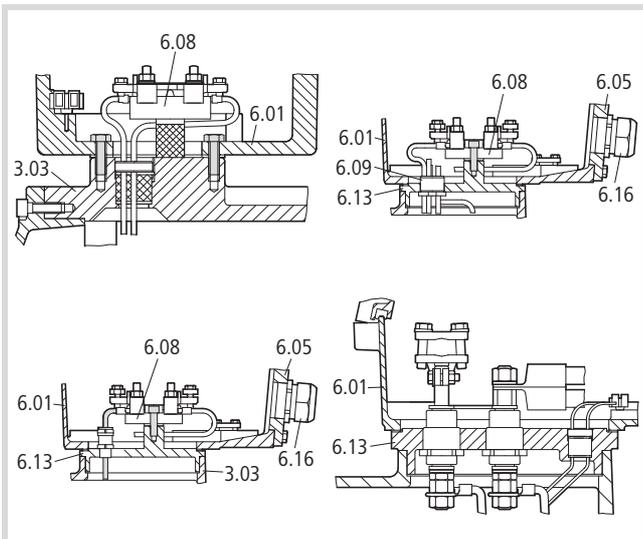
Klemmenkasten mit Schrauben befestigen
